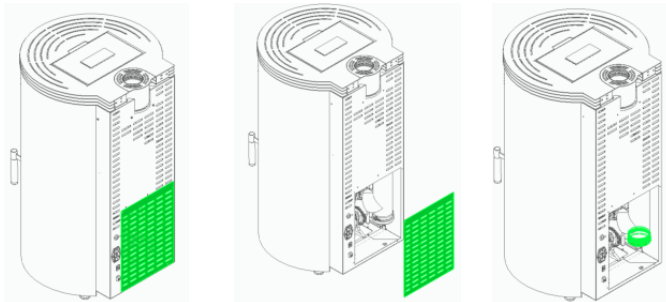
Limpieza de la "T" de inspección de la estufa E100R-UP
